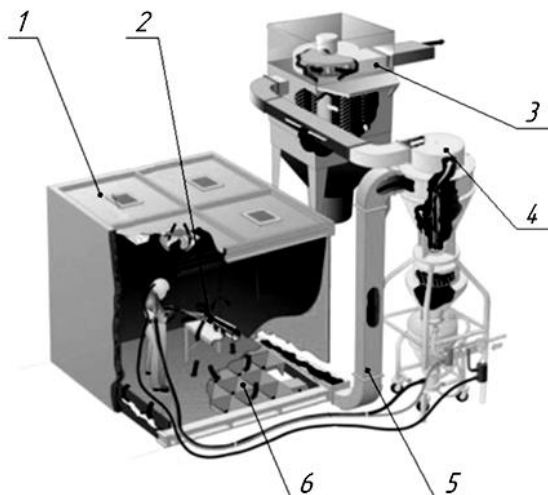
Дробеструйная камера с системой сбора дробы:
